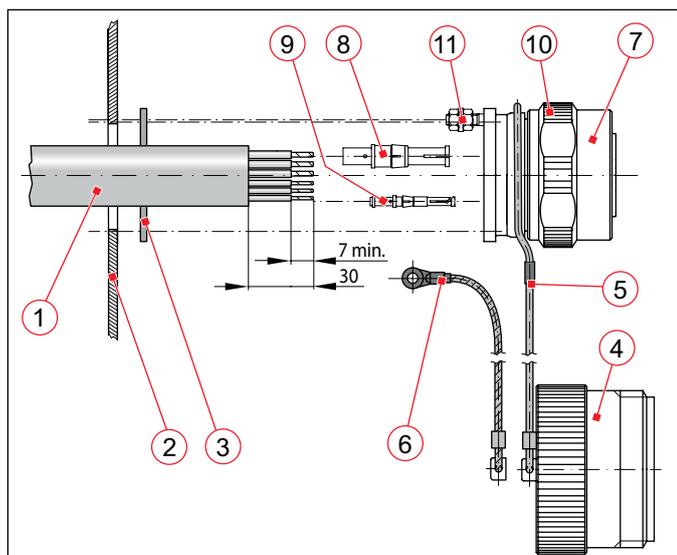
Beispiel für die Montage von Steckern mit Flansch an eine Gehäusewand
